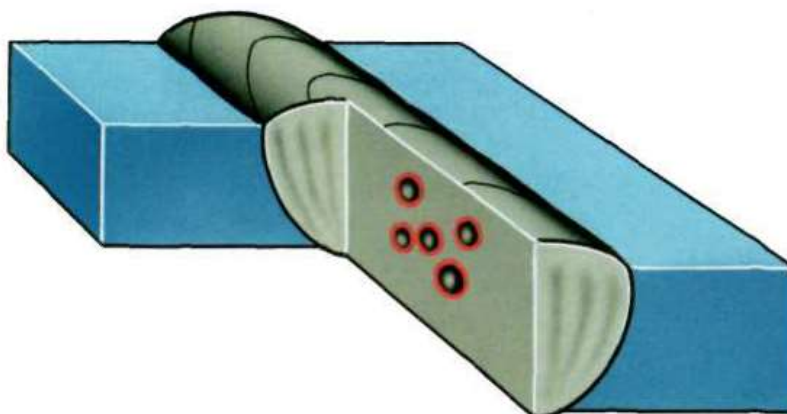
Дефекты сварного шва по типу скопления пор
